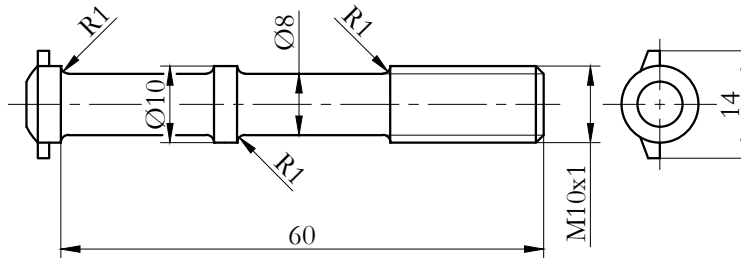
Schraube mit wechselndem Querschnitt
